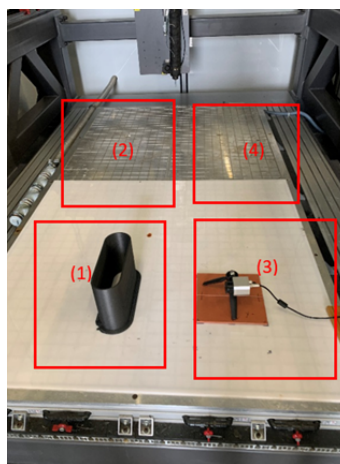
Vista de las diferentes zonas de la cama de impresión.
